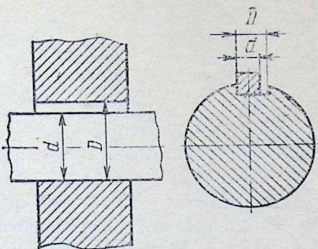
Примеры охватываемой и охватывающей поверхностей.
